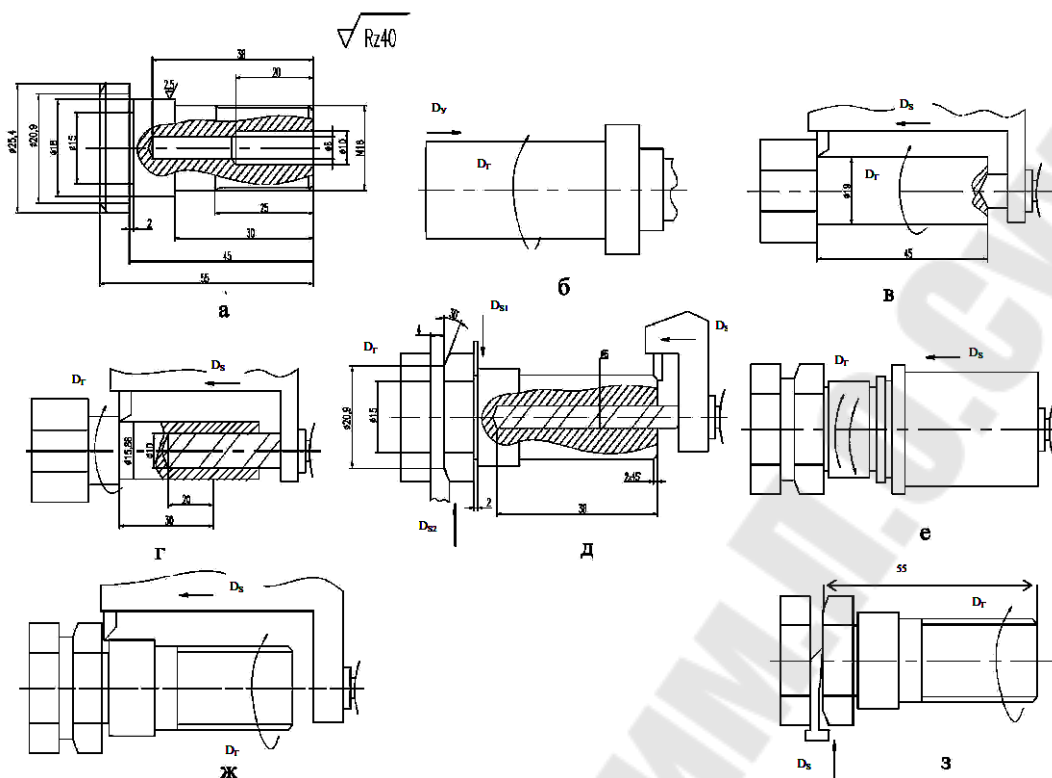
Пример обработки детали на токарно-револьверном автомате:
